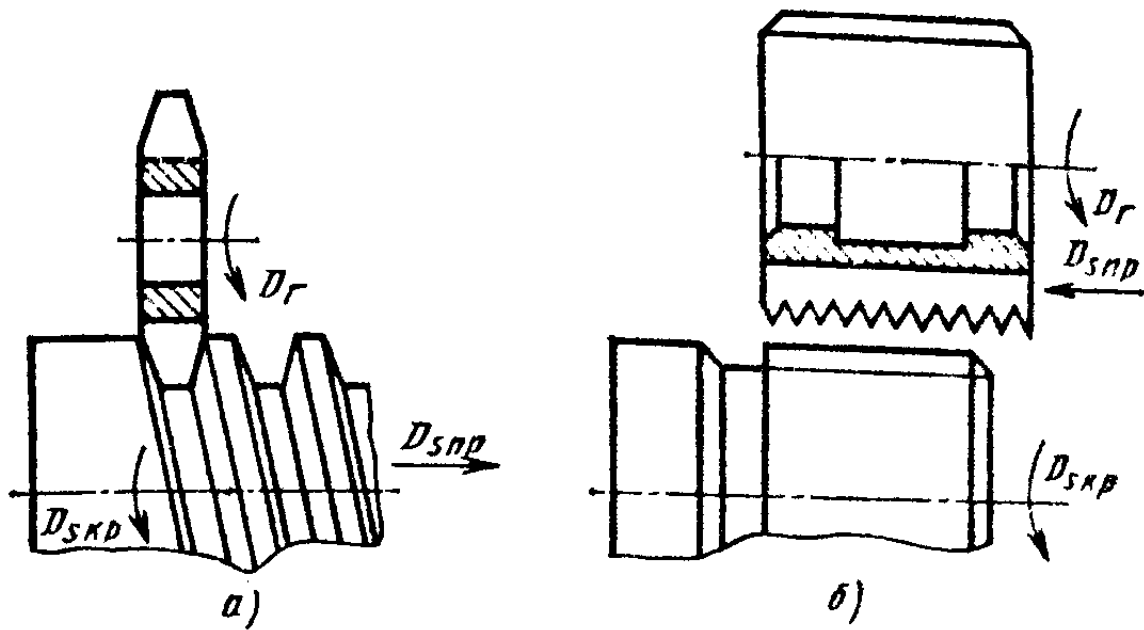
Схемы фрезерования наружной резьбы фрезой:
